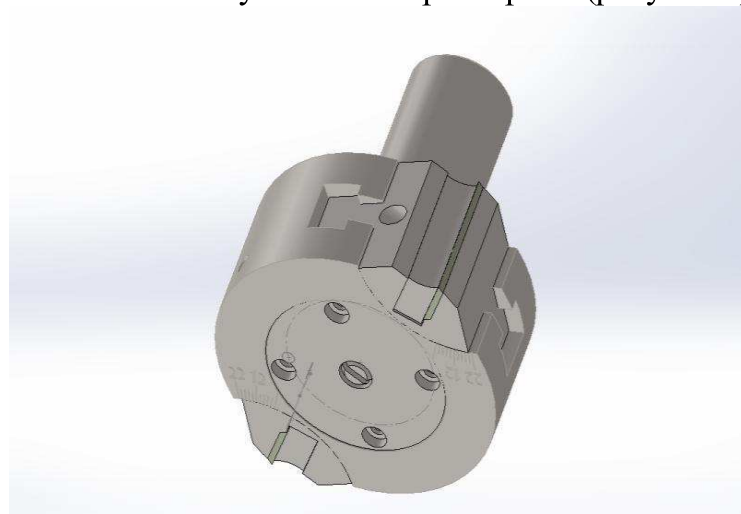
Общий вид конструкции фрезы с изменяемыми угловыми параметрами
